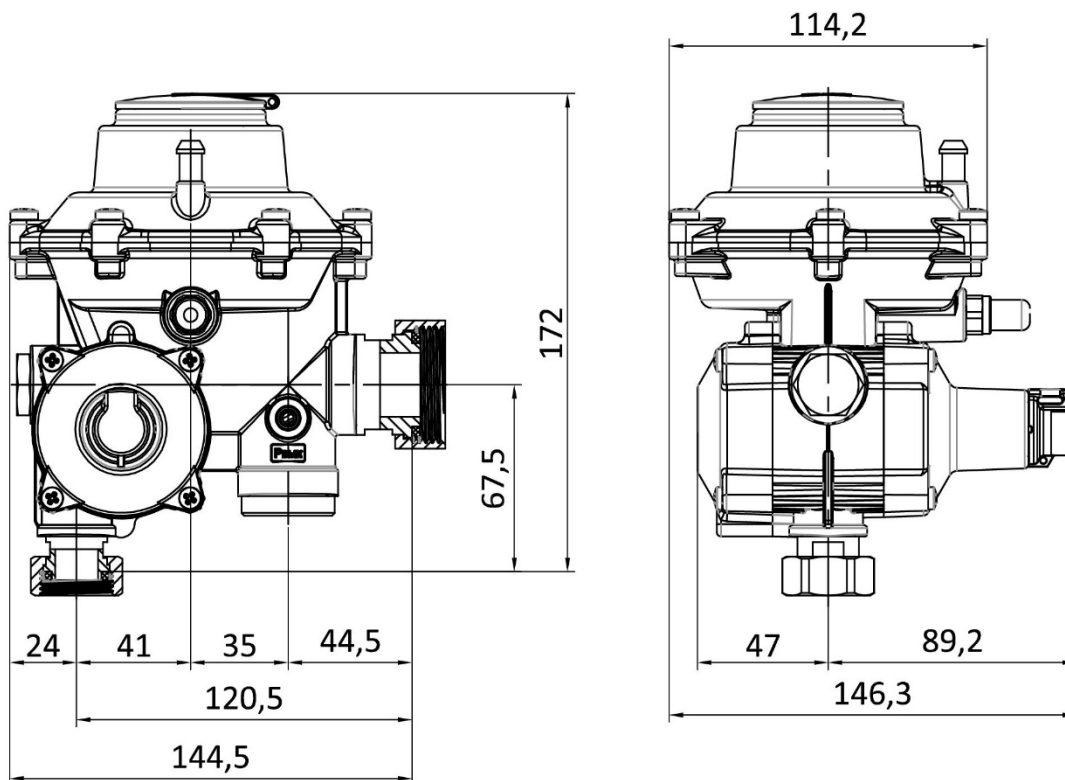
Габаритные размеры регуляторов давления «РЕД-1»
